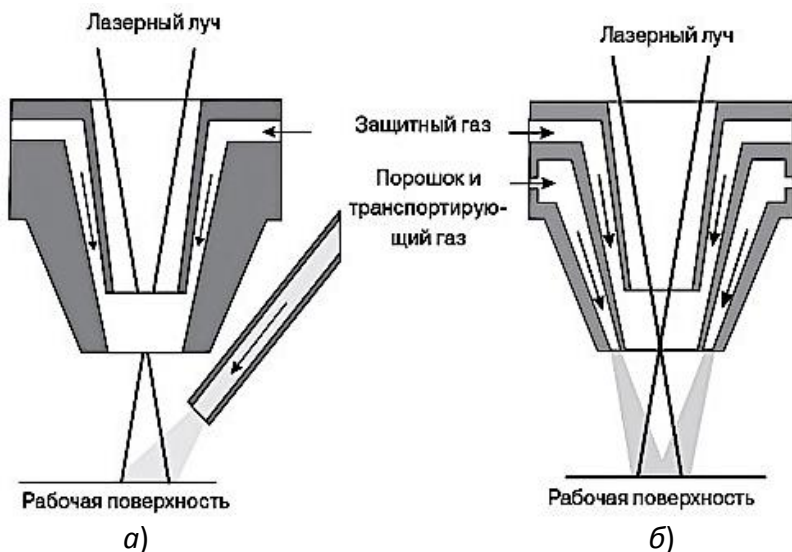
Схемы лазерной наплавки с боковой подачей порошка (а) и с коаксиальной подачей порошка (б)
